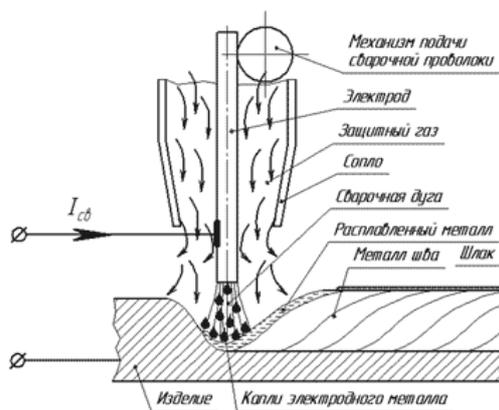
Схема сварки в защитных газах
